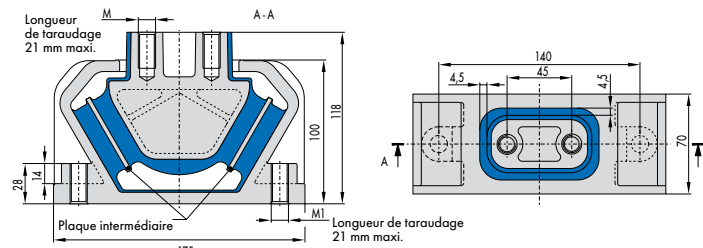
Supports cunéiformes 033 18 700, 033 18 701
